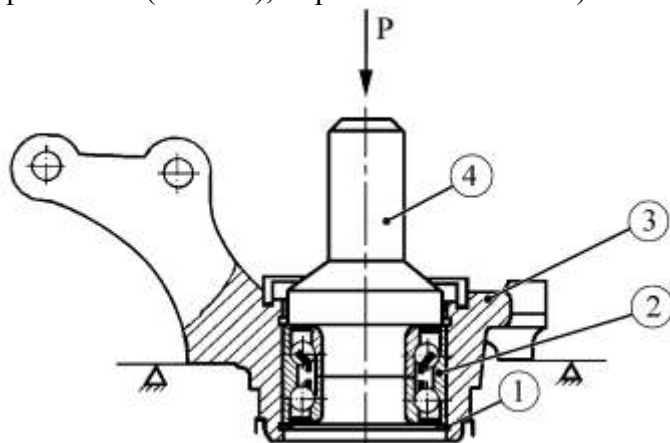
Выпрессовка из кулака и запрессовка в кулак подшипника ступицы переднего колеса:
